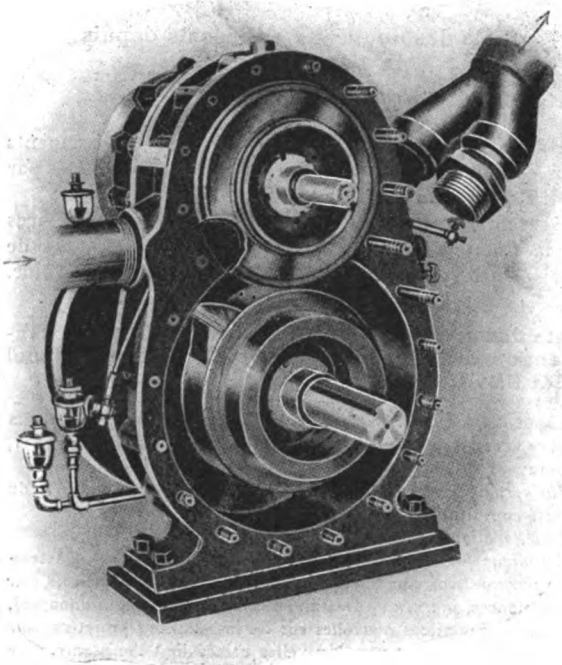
Vue intérieure de la machine rotative équilibrée Herrick (piston à l'admission).
